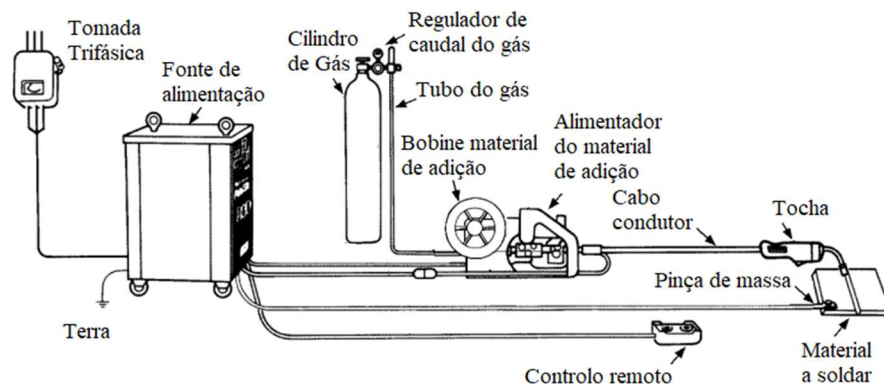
Equipamento para soldadura MIG. Adaptado de [6]
